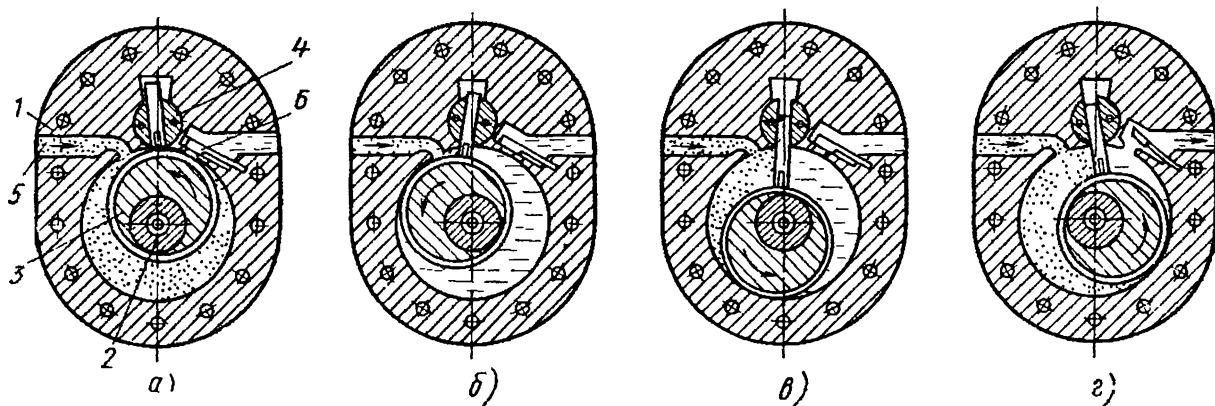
Схемы компрессора с катящимся ротором и с разделяющей пластиной, прижимаемой к ротору и скользящей в качающейся цилиндрической направляющей (фирма Эшер Вис, Швейцария):
